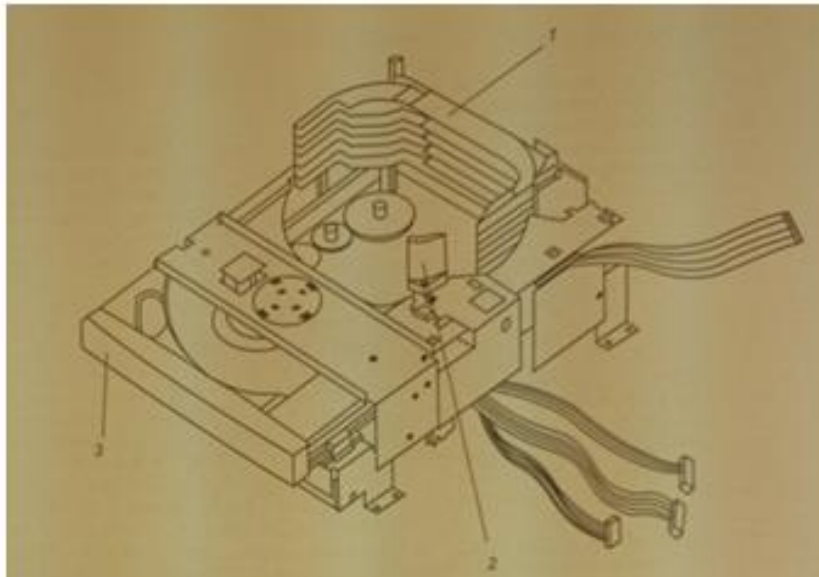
Конструкция механизма загрузки проигрывателя компакт-дисков музыкального центра Hitachi AX-S3
